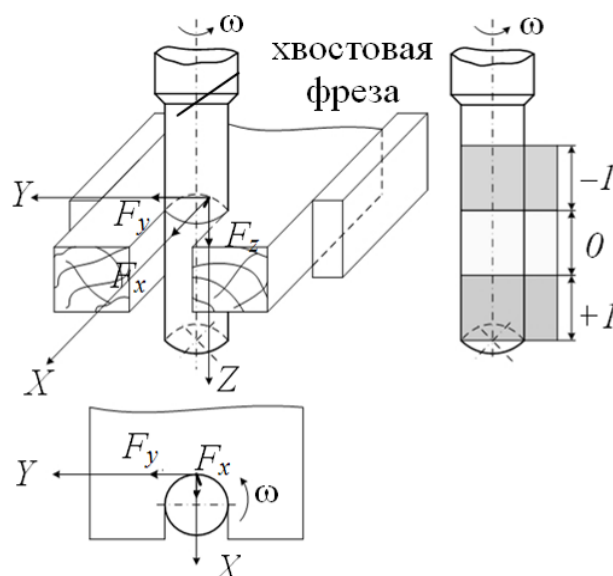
Схема обработки заготовок хвостовыми фрезами
